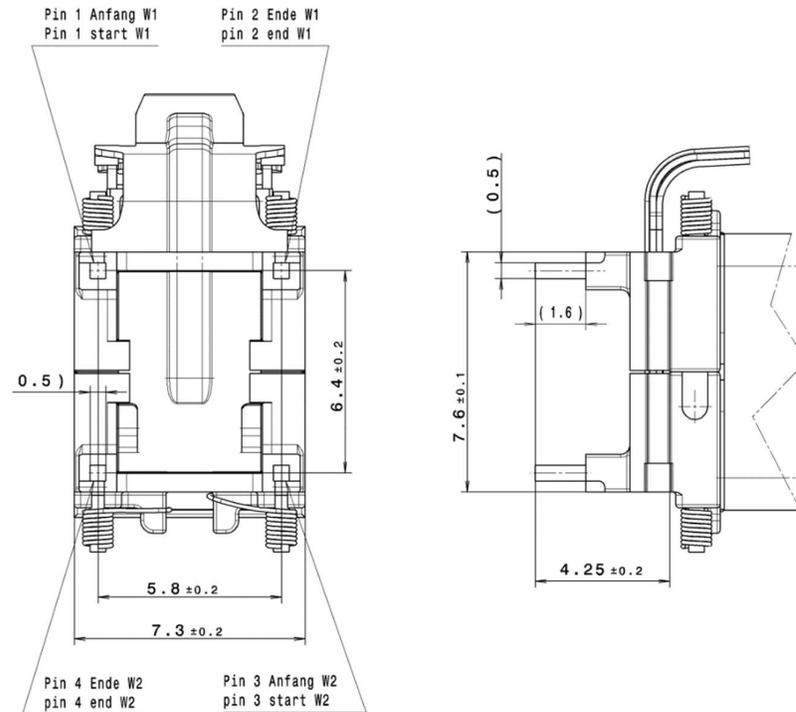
Dimension/Ausführung / Dimension/Version
